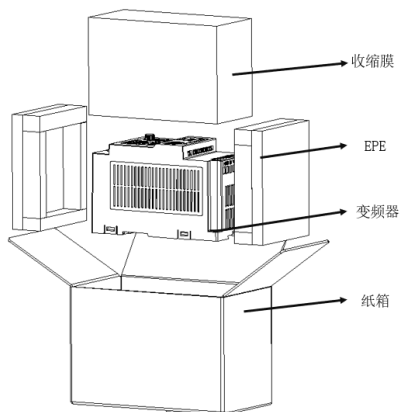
Упаковочный лист для моделей C0 - C2
